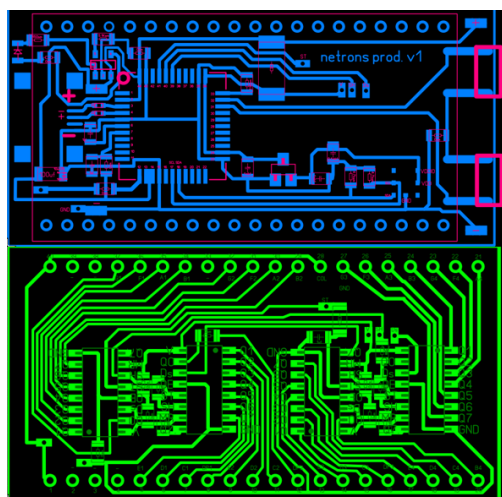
Проектирование и сборка – 2-х слойная трассировка печатной платы и сборка готового устройства
